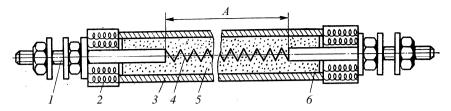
Трубчатый прямоугольный электронагреватель:
